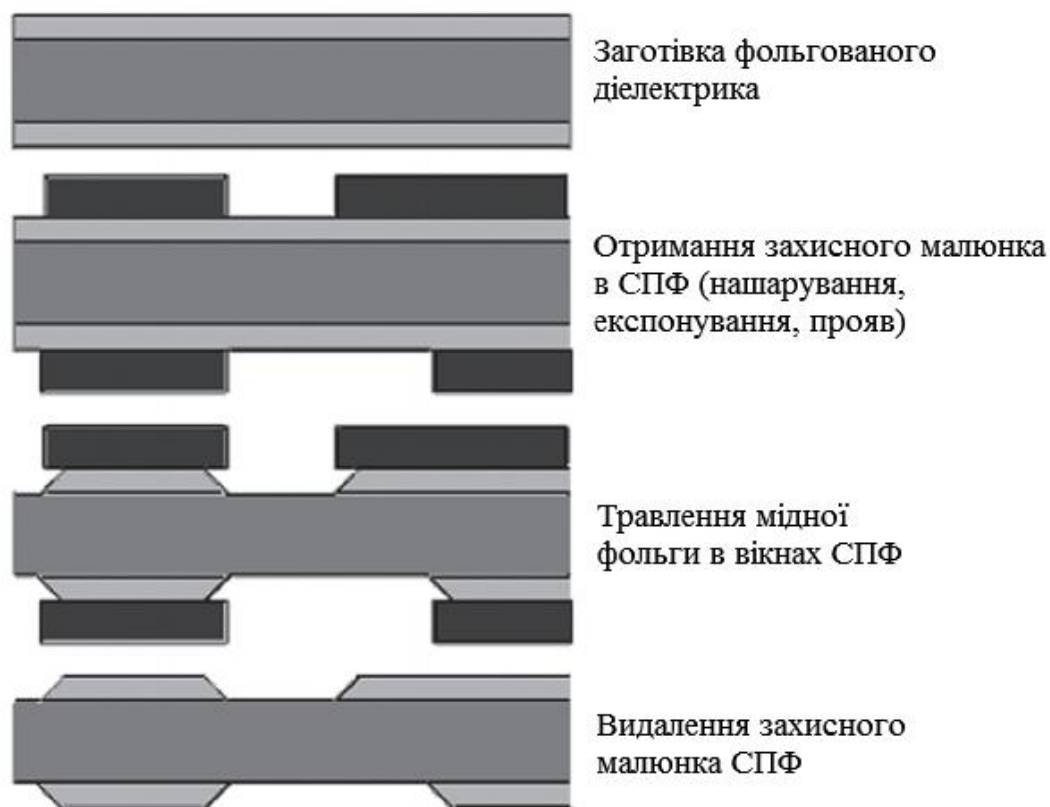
Негативний процес з використанням сухого плівкового фоторезиста
